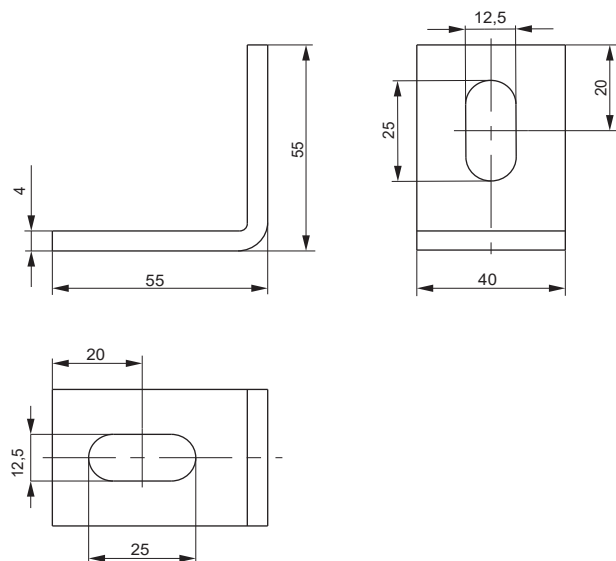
Кронштейн угловой монтажный / Figure B.6 – Angle mounting bracket
